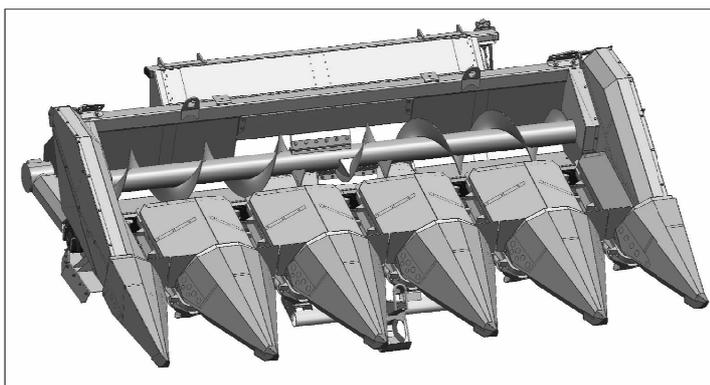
Приспособление для уборки кукурузы ППК-575 "Argus 575"
